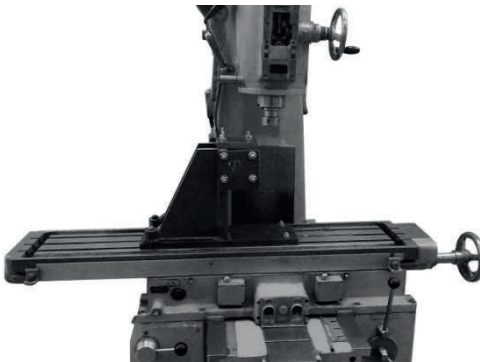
Фрезерный станок TOS FA3V с оснасткой
